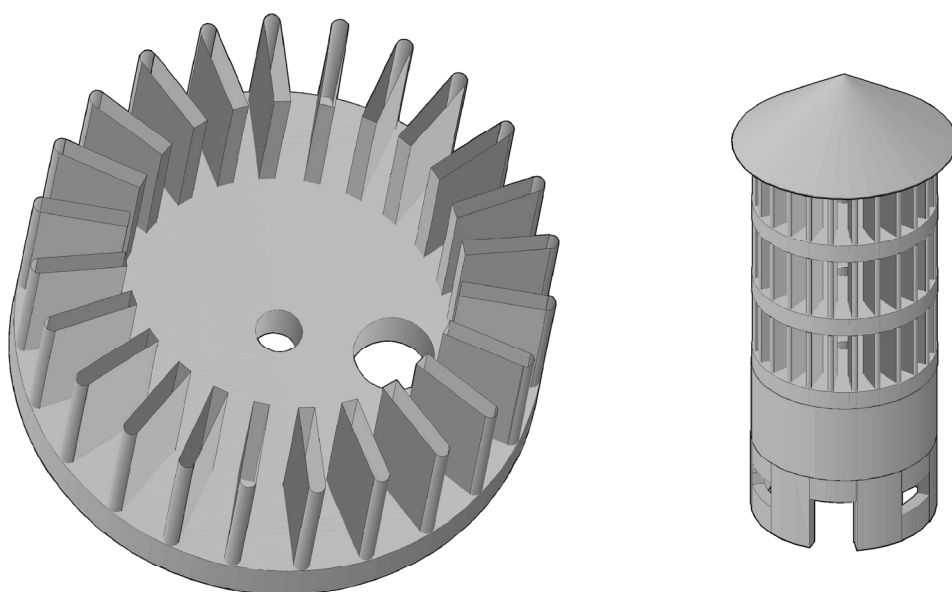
Железобетонная внешняя конструкция ветроустановки и ее отдельное звено
